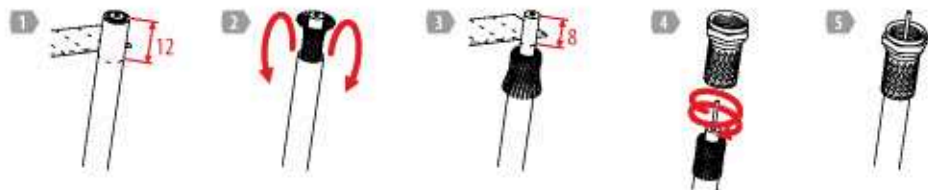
Разделка коаксиального кабеля и установка F-разъема
